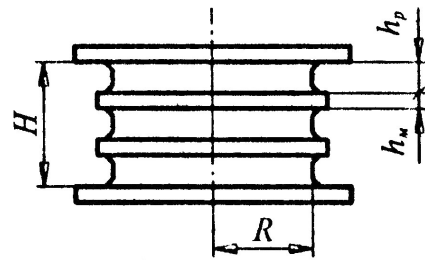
Резинометаллический трехэлементный виброизолятор роторной дробилки типа Бармак В9000×НД
